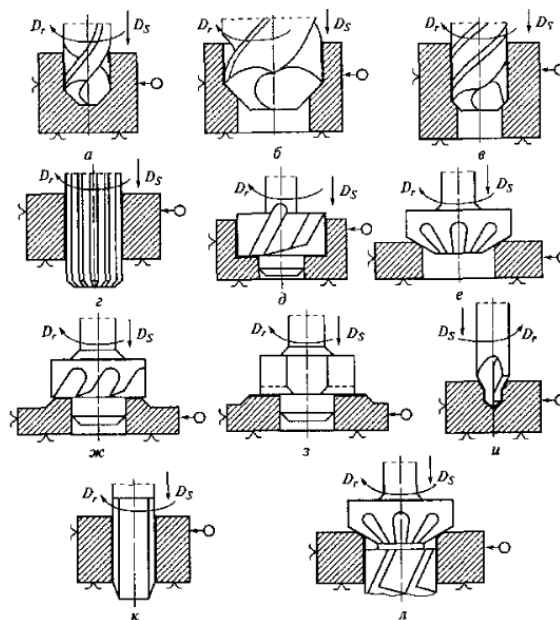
Інструменти та схеми обробки отворів на свердлильних верстатах
